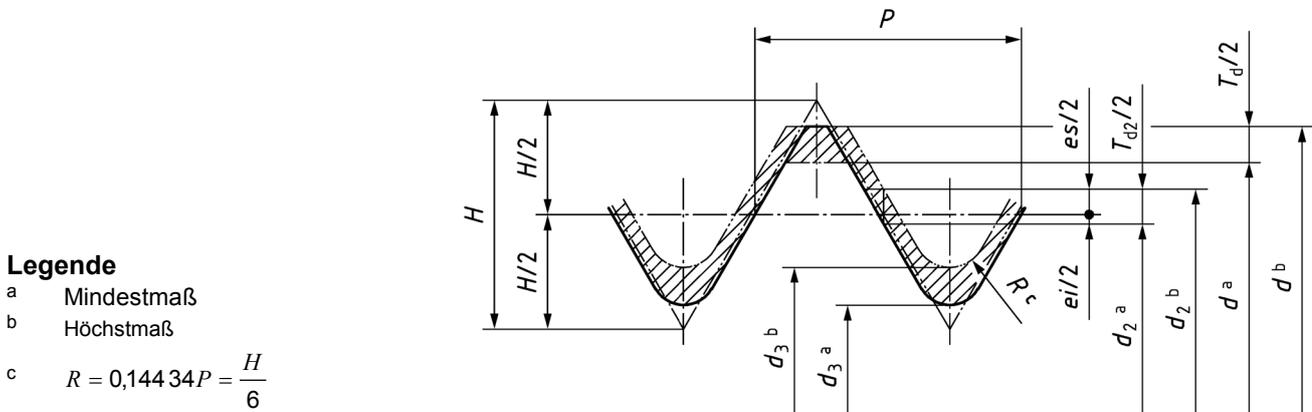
Außengewinde mit positivem oberem Grenzabmaß es und negativem unterem Grenzabmaß ei im Flankendurchmesser; Toleranzfeldlage Sk 6
